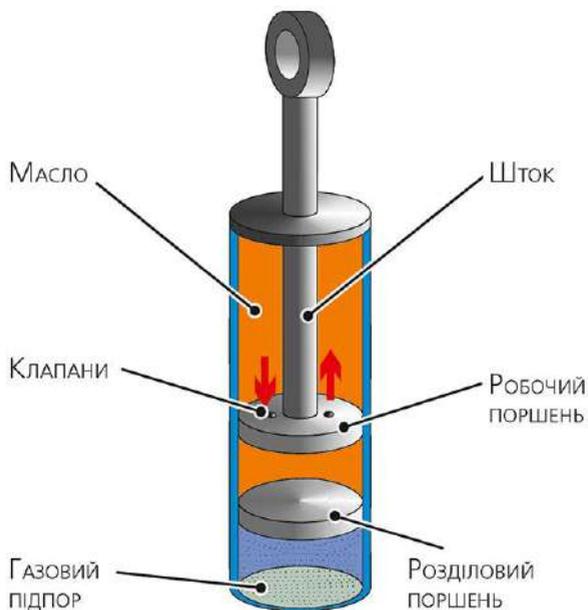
Однотрубний газонаповнений амортизатор
